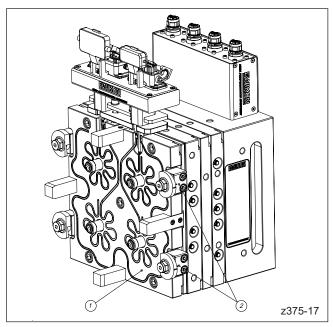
Werkzeug mit Schnellspannvorrichtung
